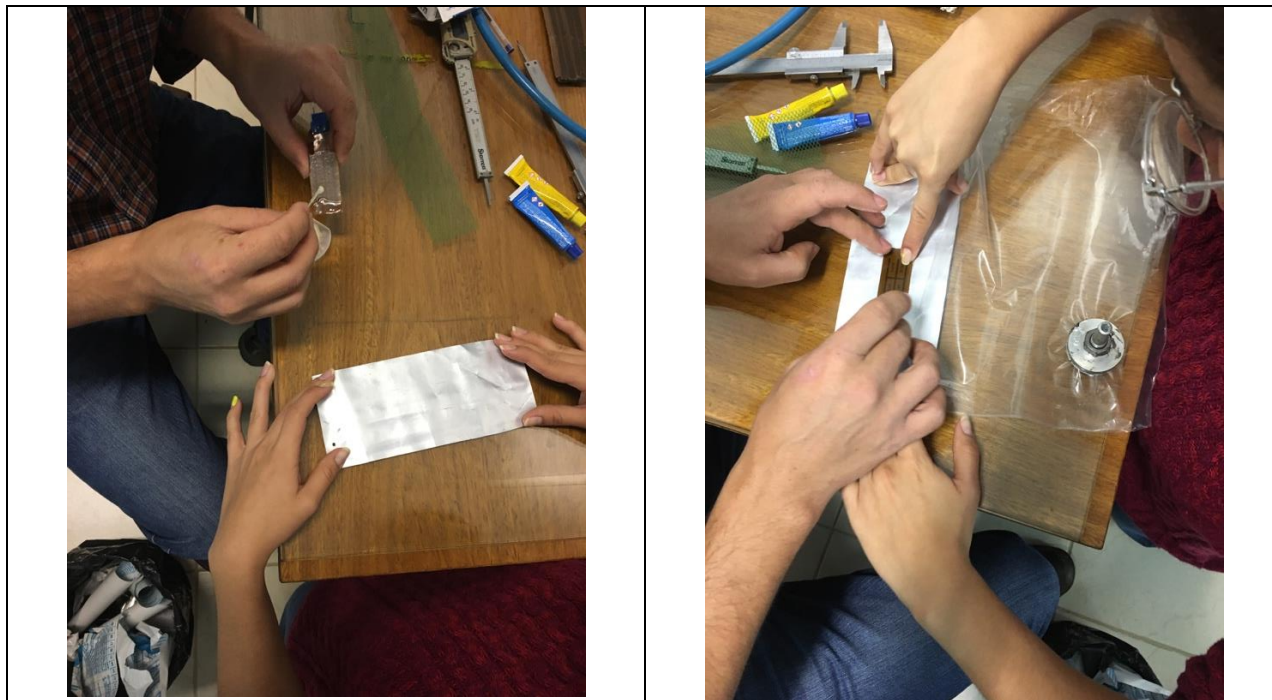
Geometría cilíndrica con placa de aluminio. Fuente: Autor
